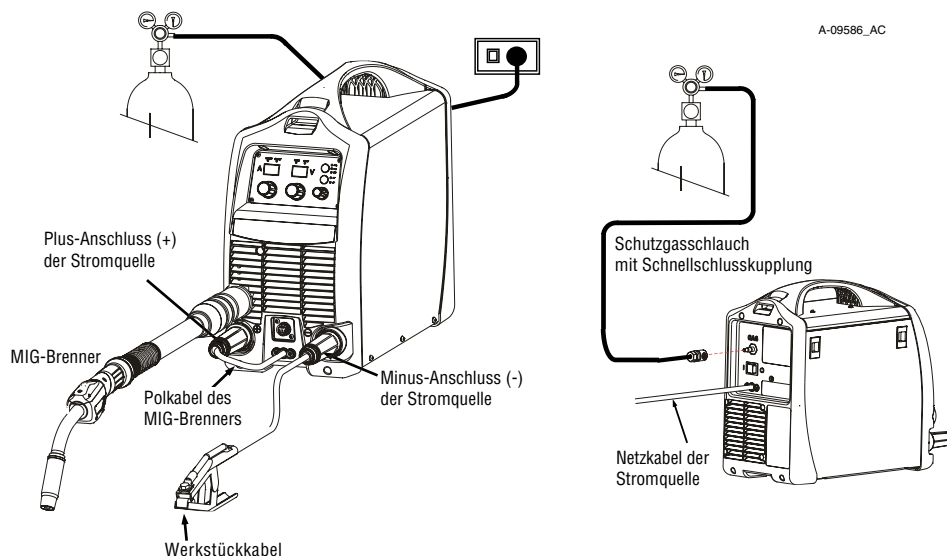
Konfiguration für MIG-Schweißen mit MIG-Schweißdraht unter Schutzgas
